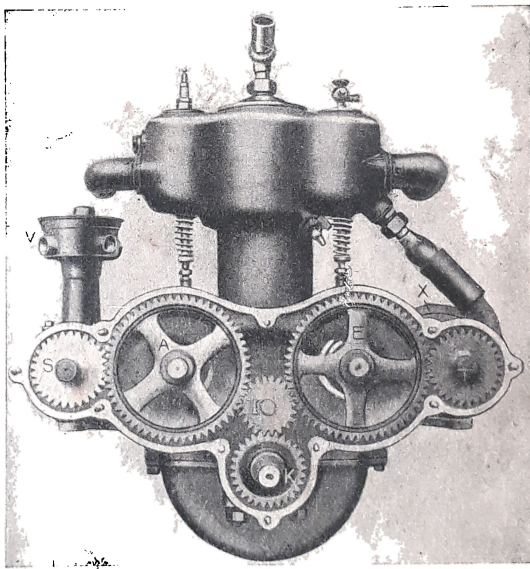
Vista e sezione di un motore a più cilindri con disposizione simmetrica delle valvole.
